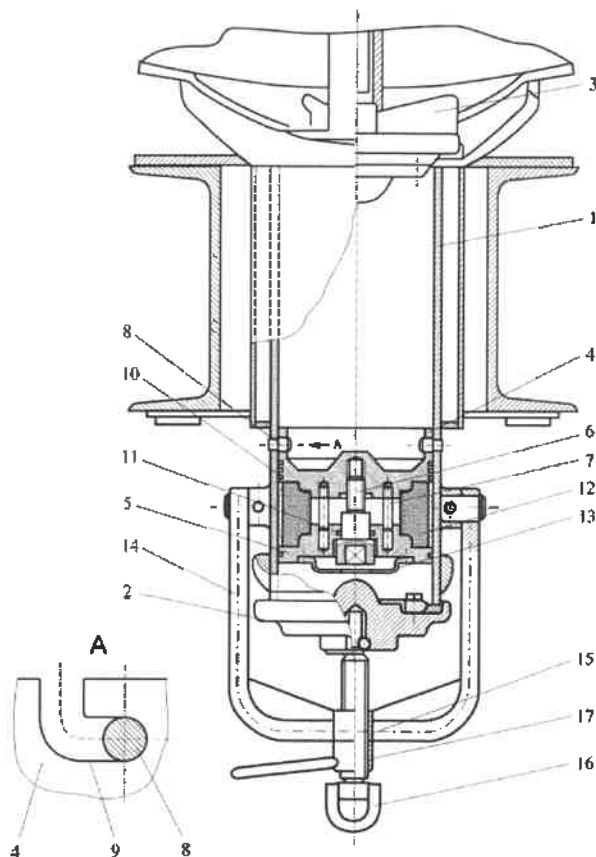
Конструкция сливного прибора с тройной защитой [9]
